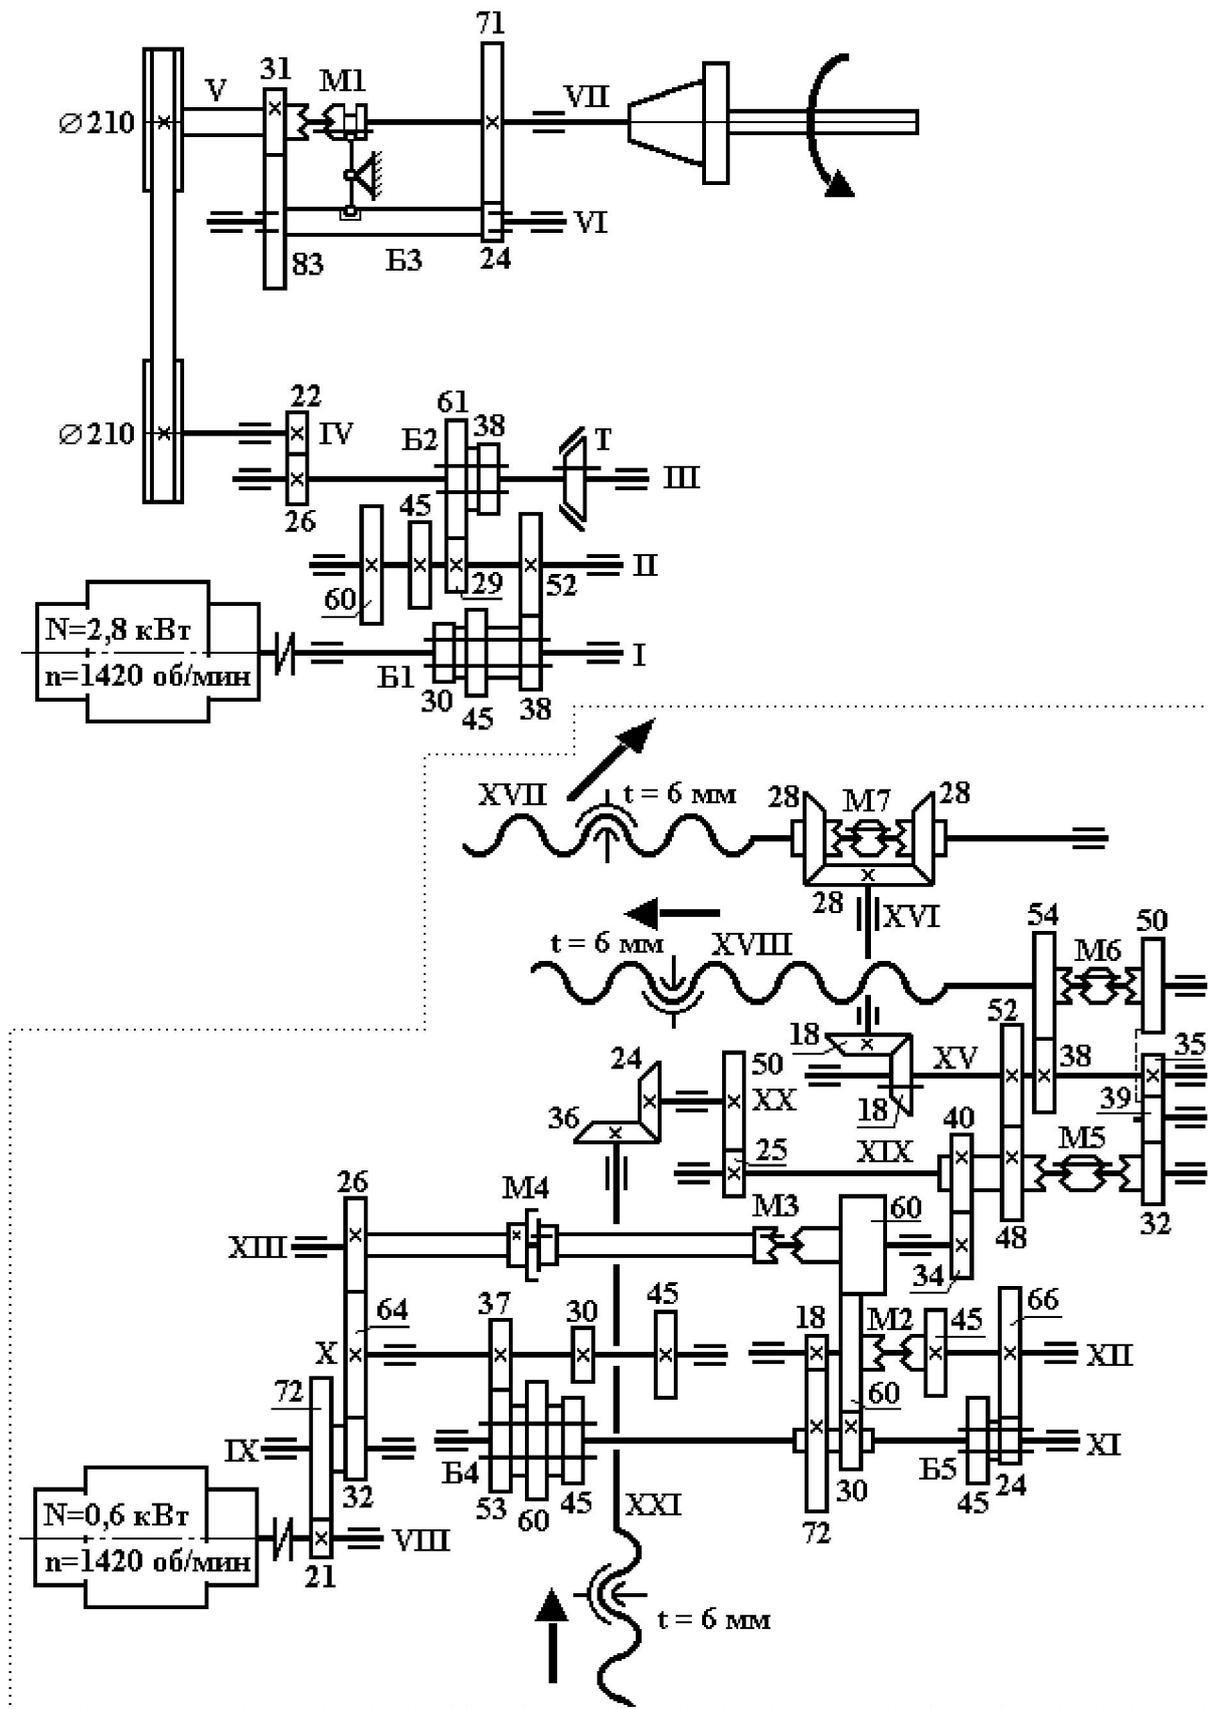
Кинематическая схема горизонтально-фрезерного станка модели 6М80Г
